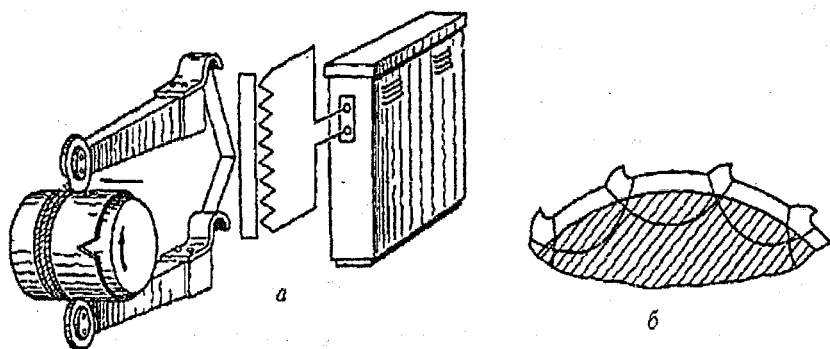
Схема приварювання металевої стрічки до поверхні вала: а – джерело живлення; б – перекриті імпульси
